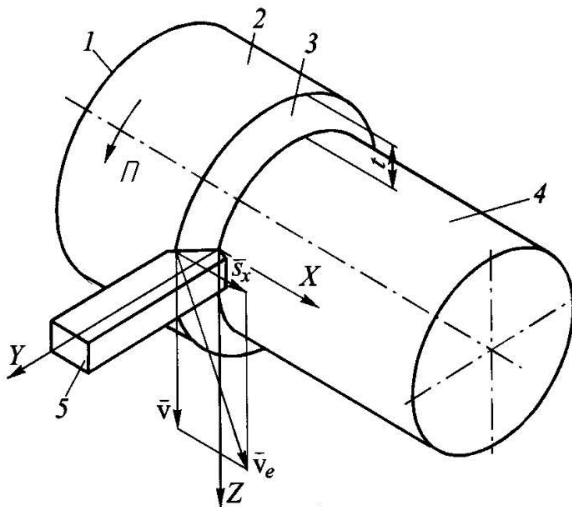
Поверхности заготовки при токарной обработке проходным резцом
